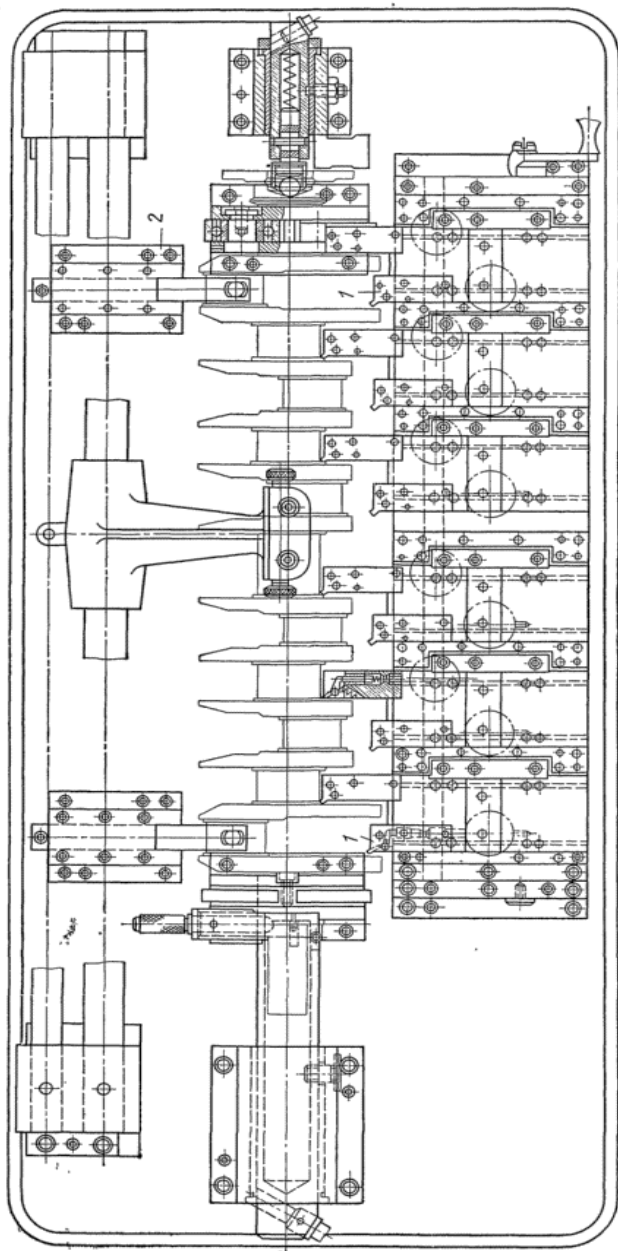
Приспособление для контроля основных размеров коленчатого вала
